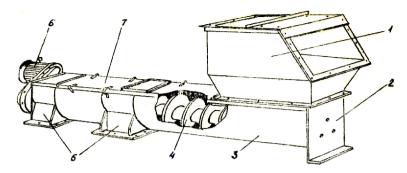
Общий вид загрузочного шнека ШЗС-40М: 1 –приёмный бункер; 2 – боковина; 3 – кожух; 4 – шнек; 5 – горловина выгрузная; 6 – мотор-редуктор; 7 – крышка
